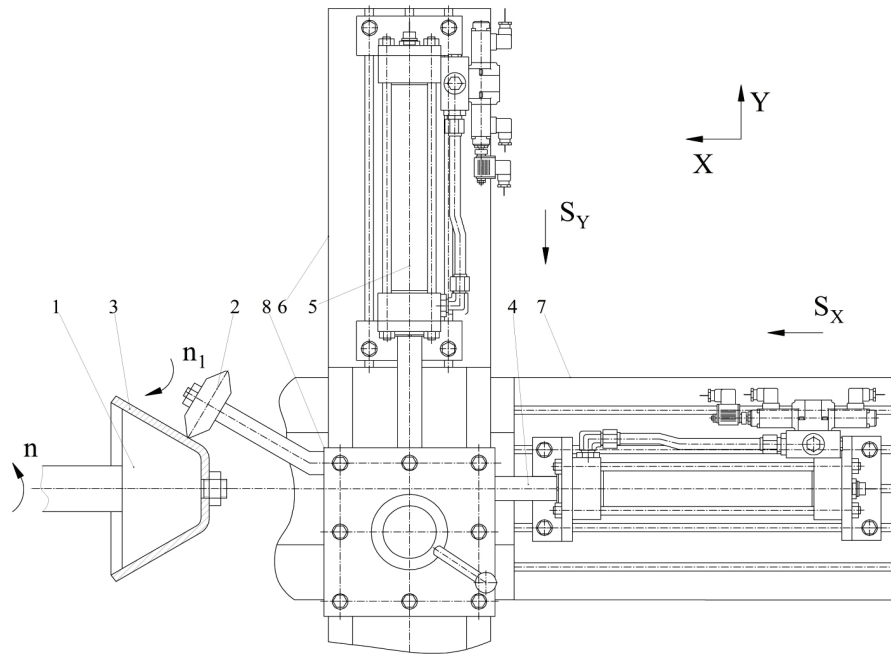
Схема пристрою з мехатронним приводом для виготовлення деталі ротаційною витяжкою
